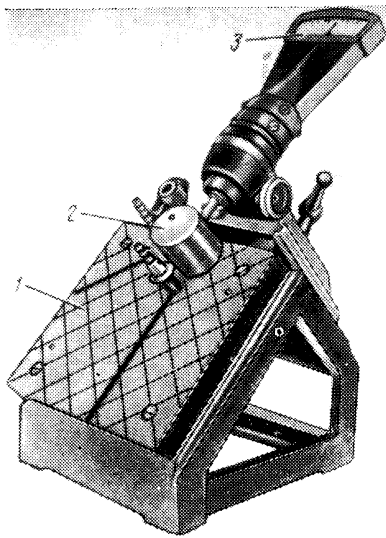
Прибор для проверки перпендикулярности цилиндрической поверхности ролика относительно его торца:
